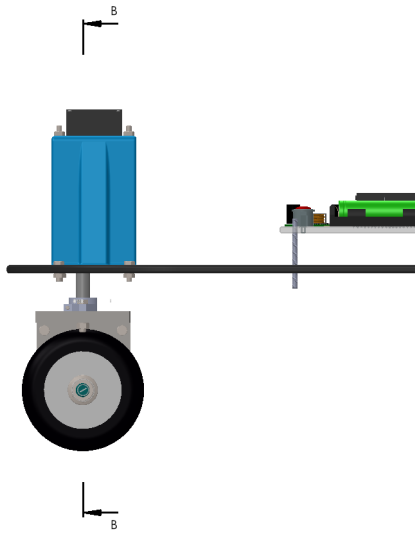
Plan de coupe au niveau du moyeu de la roue avant
